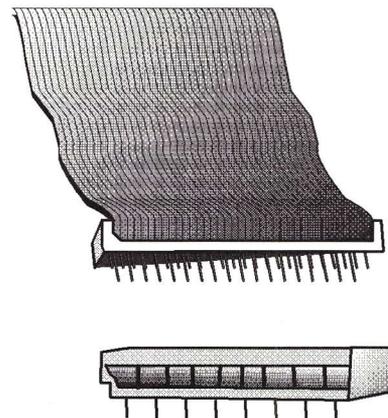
Connecteur câble plat pour soudage sur circuit imprimé
